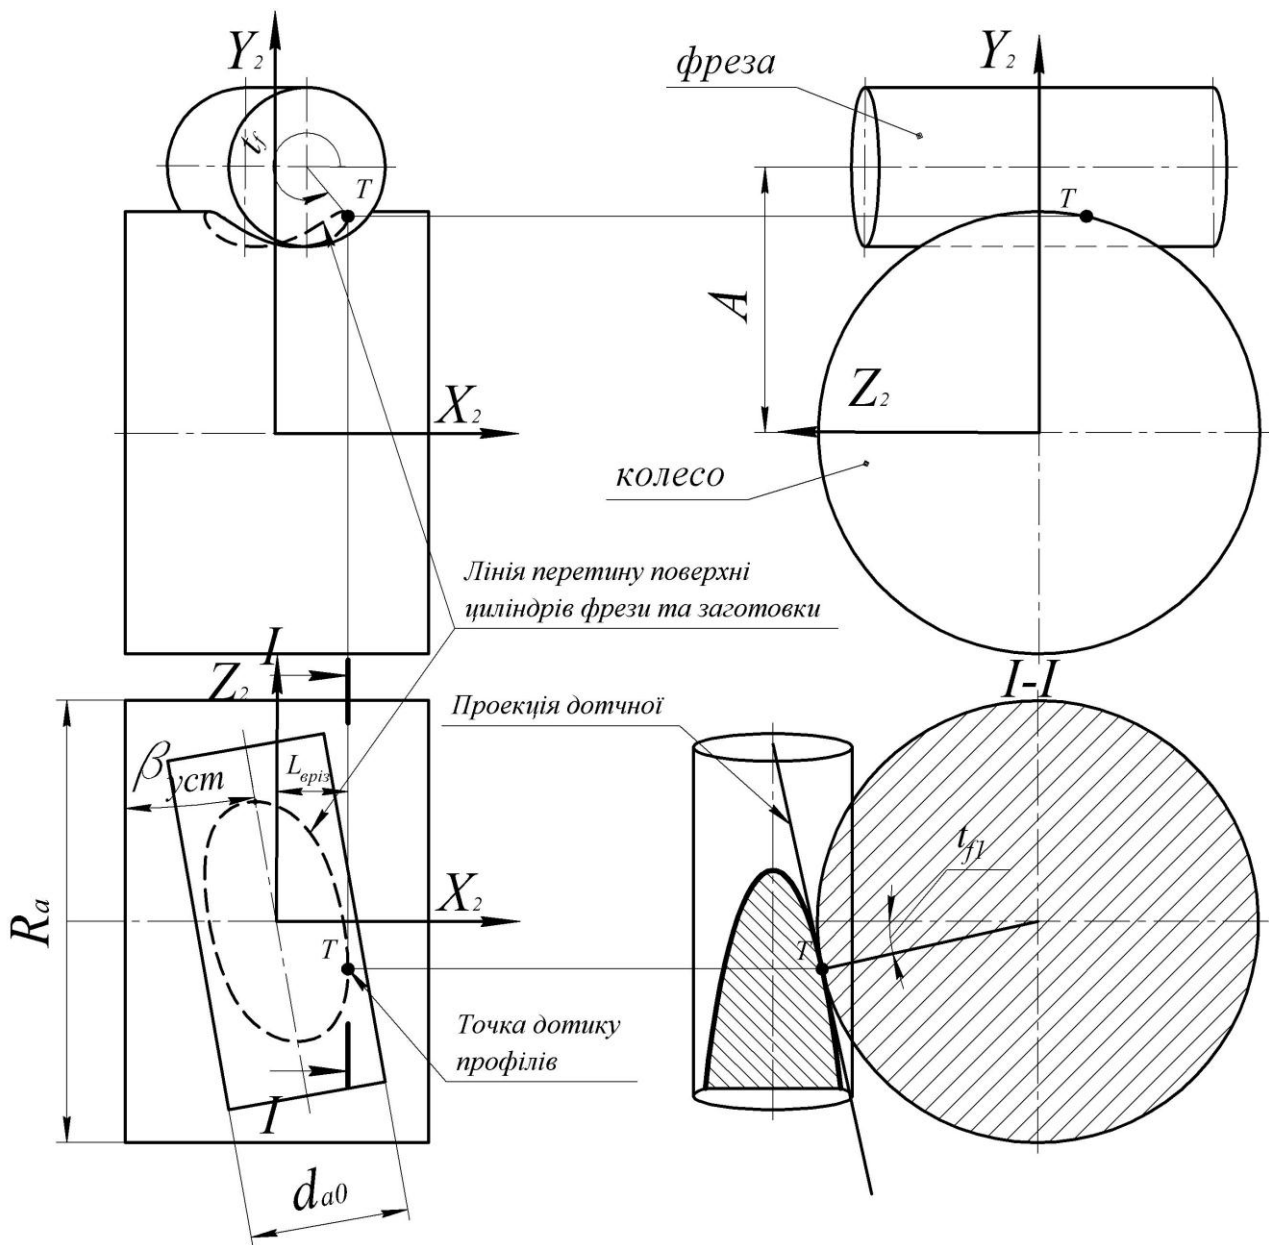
Схема розрахунку положення врізання фрези в заготовку
